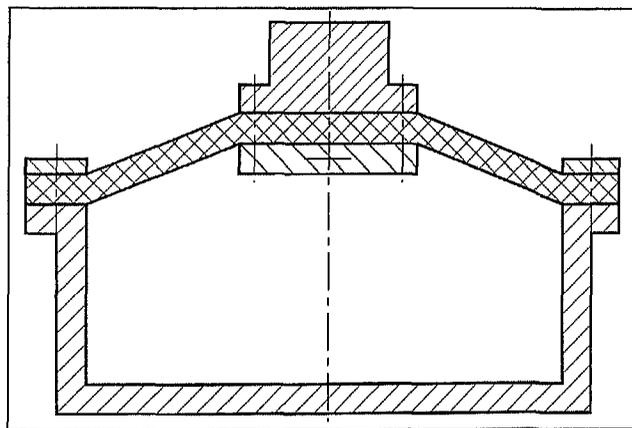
Пневматический амортизатор для виброизоляции прессов
